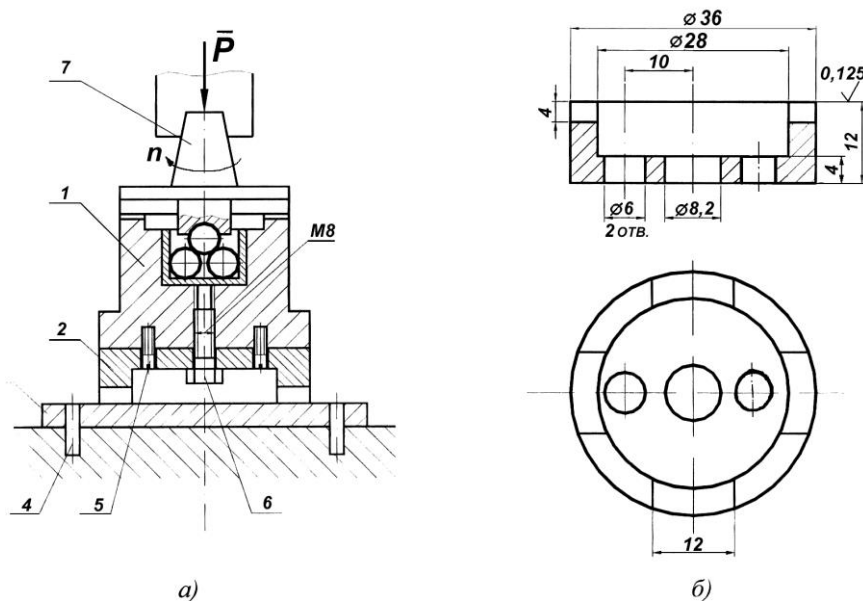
Схема кріплення та конструкція зразка при випробуванні (тертя ковзання). 1 – корпус; 2 – зразок; 3 – контртіло; 4 – штифтове з'єднання; 5 – шпилька; 6 – гвинт; 7 – хвостовик.
